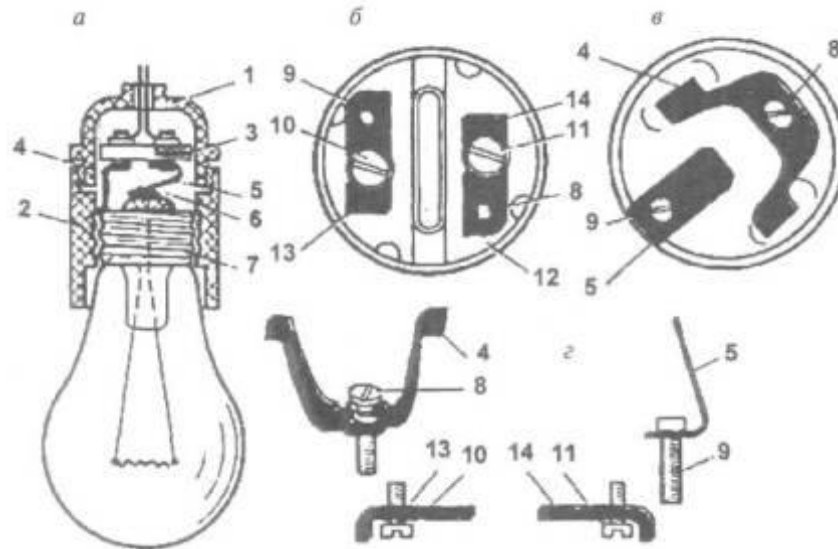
Різьбовий патрон для ЛН с цоколем E27:
